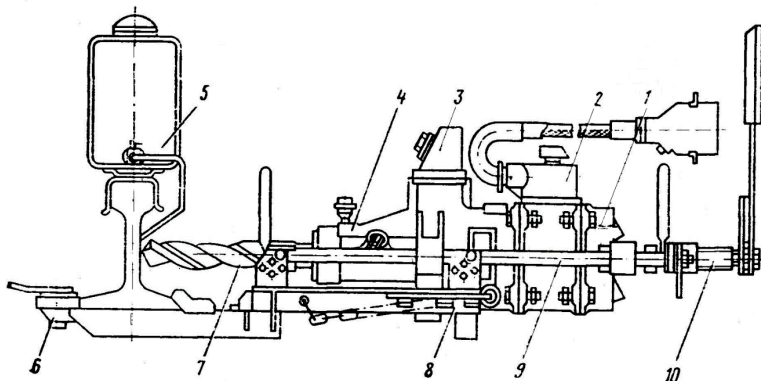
1. 9. Рейкосвердлувальний станок типу 1024Б:
